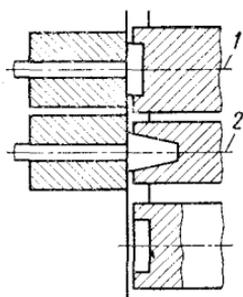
Схема штампов двухпозиционного холодновысадочного автомата с двумя линиями подачи:
